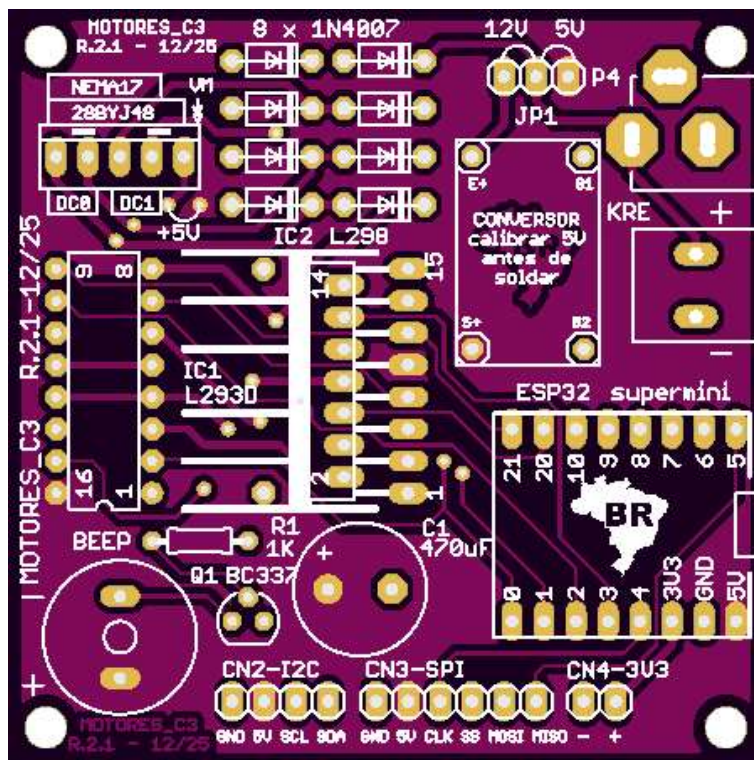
Placa MOTORES_C3 rev. 2.1 (lado dos componentes)
